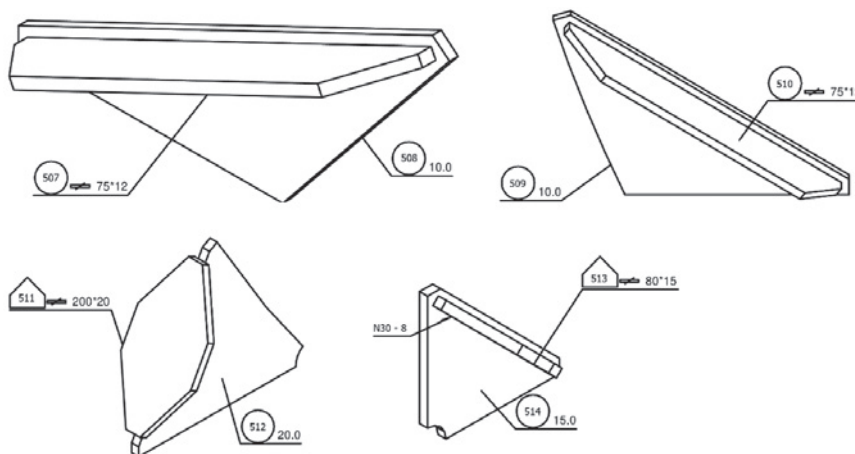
Примеры узлов сборок книц с приварными фланцами
